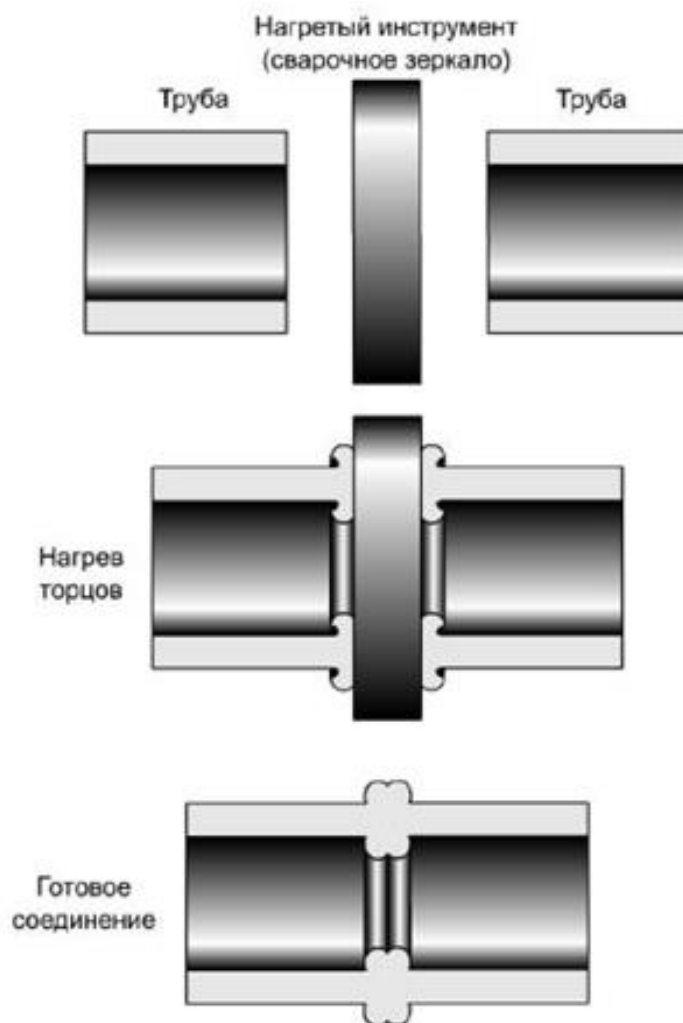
Последовательность сварки встык нагретым инструментом
